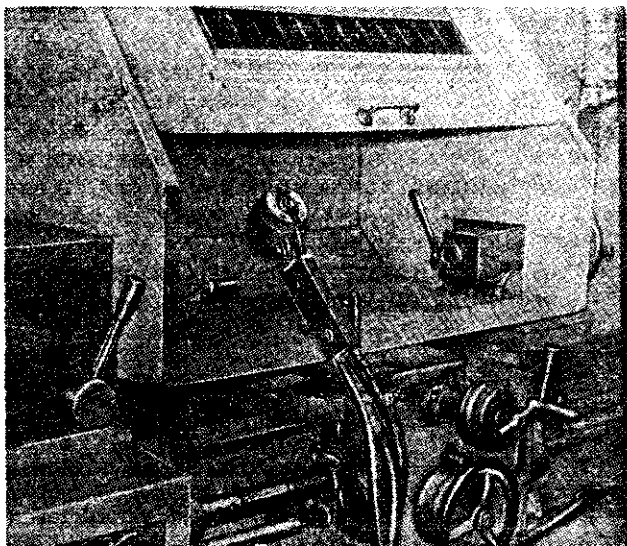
Плазменное напыление толкателя (в рабочем положении подводится заглушка пяты, установленная на задней бабке)
